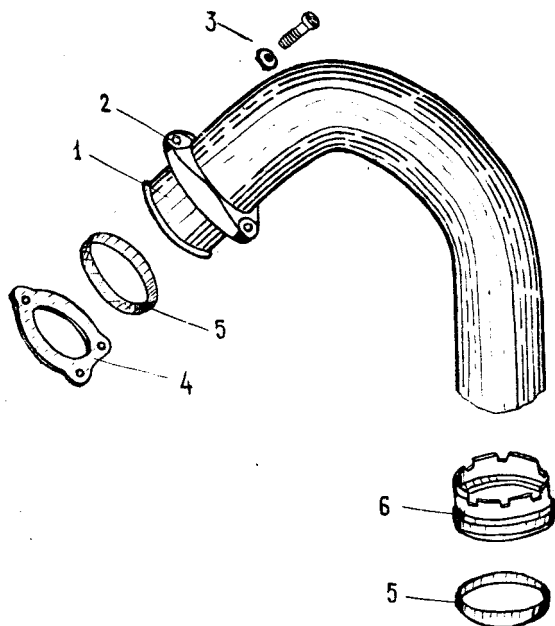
Впускная труба: 1—впускная труба; 2—фланец; 3—винт крепления фланца; 4—паронитовая прокладка; 5—резиновое уплотнительное кольцо; 6—гайка
